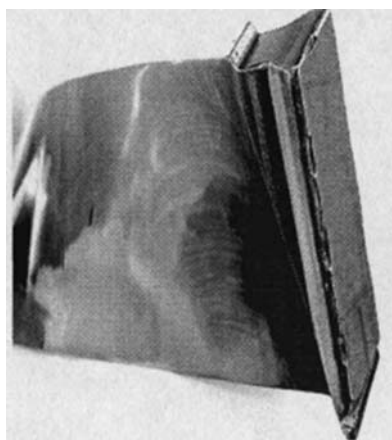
Замок лопатки, восстановленный аргонодуговой наплавкой
